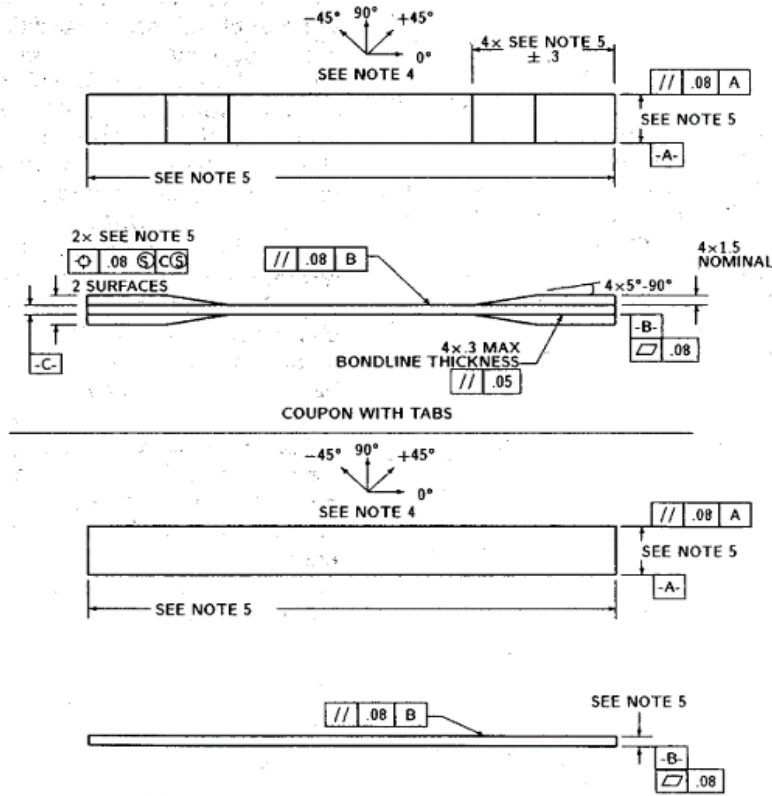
Dimensionamiento de probetas en base a la norma ASTM D-3039.
